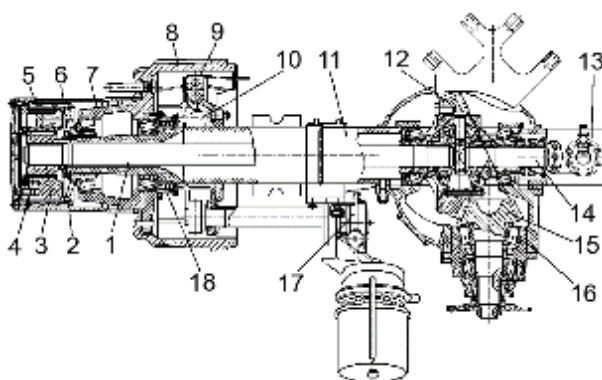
Задний мост КАМАЗ: 1 – левая полуось; 2 – ступица коронного зубчатого колеса колесной передачи; 3 – водило с кожухом и сателлитами; 4 – солнечное зубчатое колесо колесной передачи; 5 – коронное зубчатое колесо колесной передачи; 6 – гайка подшипников; 7 – ступица заднего колеса; 8 – тормозной барабан; 9 – задний левый тормозной механизм; 10 – датчик скорости с кронштейном; 11 – картер заднего моста; 12 – ведомое коническое зубчатое колесо; 13 – механизм блокировки; 14 – правая полуось; 15 – ведущее коническое зубчатое колесо; 16 – главная передача заднего моста; 17 – регулировочный рычаг; 18 – ротор датчика
